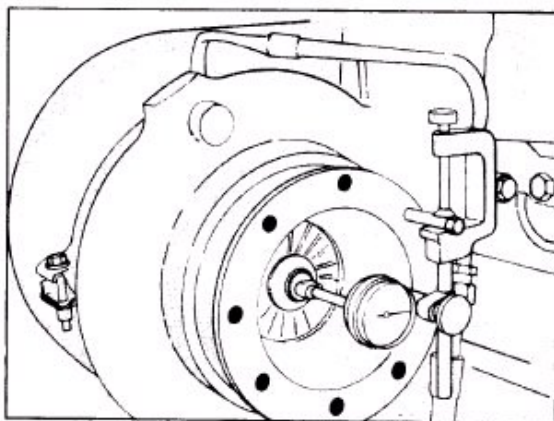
(OM1065L) Проверка подшипника и зазора турбокомпрессора.
